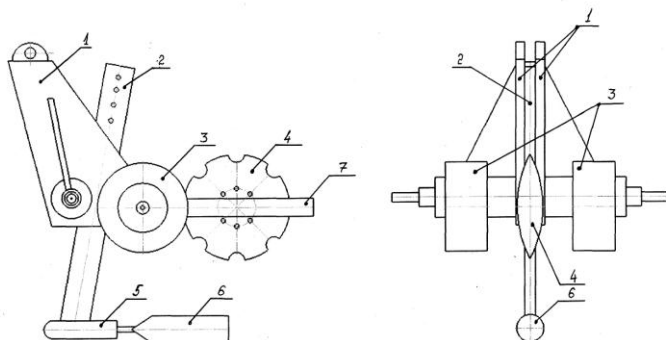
Конструкция кротователя-бороздодела КБН-1.
